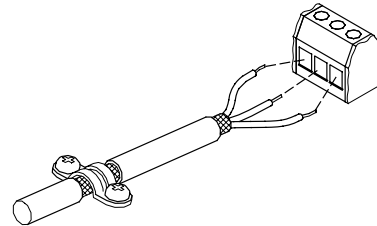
Соединение оплетки и проводов экранированного кабеля с колодкой
